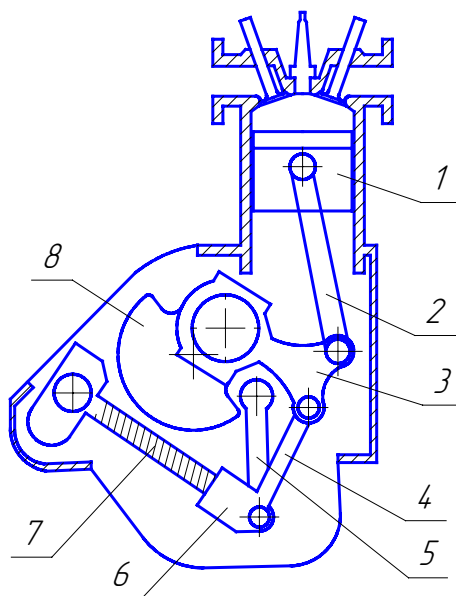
Схема двигателя с переменным ходом поршня конструкции Н. Pouliot [117]:
